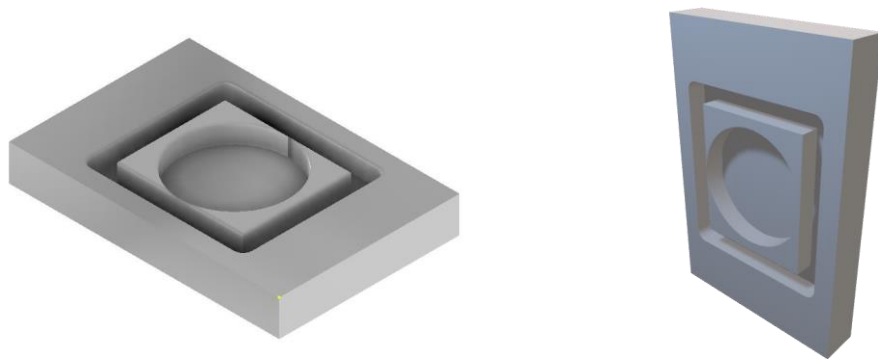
Τρισδιάστατη απεικόνιση αποστολής 27
